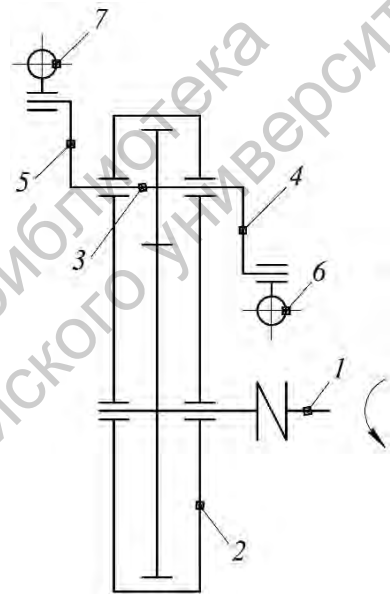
Схема механизма для двухтросового привода рабочего оборудования
